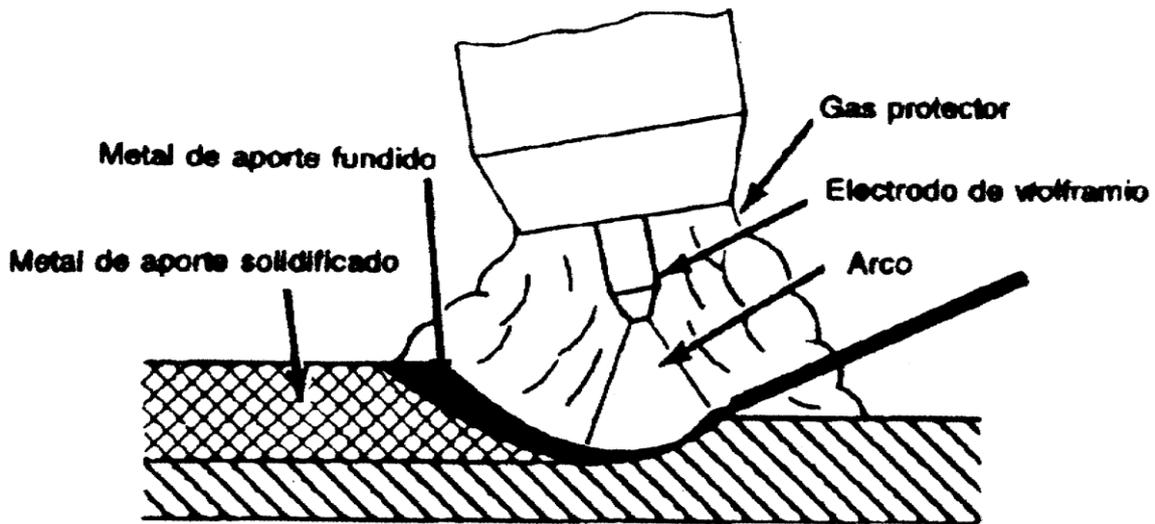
3. Procedimiento de soldadura GTAW-TIG.
